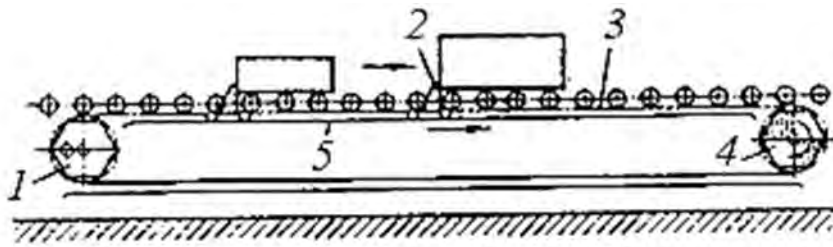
Вертикально замкнутый грузоведущий конвейер для перемещения грузов по стационарным роликам: 1 – натяжная звездочка; 2 – толкатель; 3 – тяговая цепь; 4 – приводная звездочка; 5 – направляющий путь
